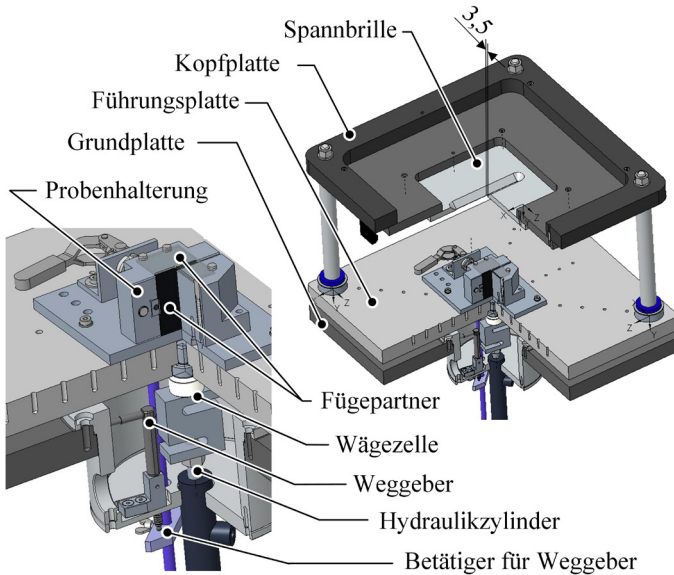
Viersäulen-spanntechnik, bestehend aus Grund-, Führungs- und Kopfplatte mit integrierter Spannbrille (rechts), sowie eine Schnittansicht mit Kunststoffproben, Probenhalterung, Wägezelle, Weggeber und Hydraulikzylinder
